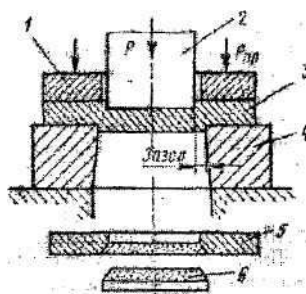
Схема вырубki (пробивки): 1 - прижим; 2 - пуансон; 3 - заготовка; 4 - матрица; 5 - отход (изделие); 6 - изделие (отход)
